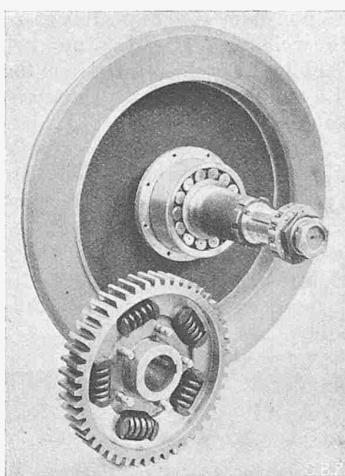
Triebrad mit gefedertem Zahnkolben.
